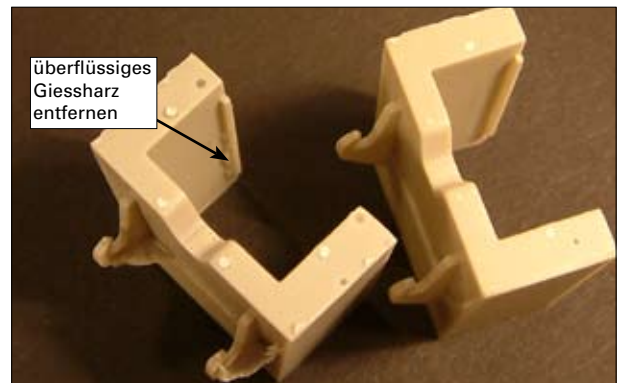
Unbearbeitetes neben einem bearbeiteten Gegengewicht
